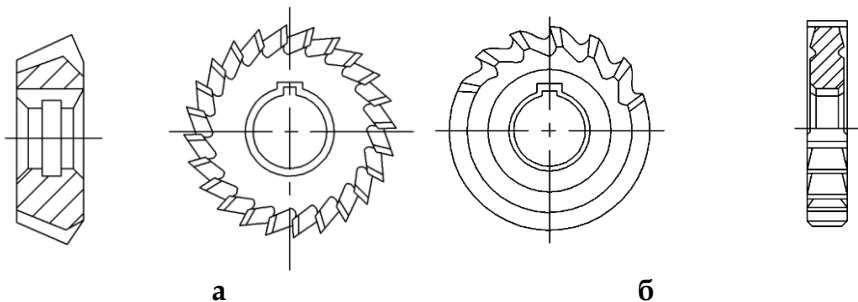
Кутові фрези: а – однокутова; б – двокутова
